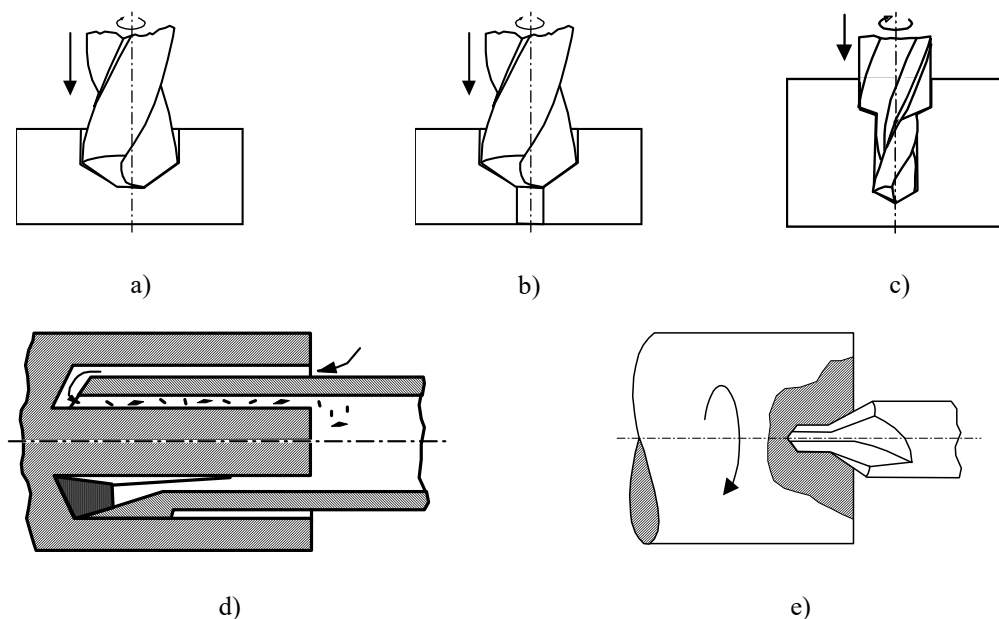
Exemplos de furação (Adaptado de [3]) – a) Furação a cheio, b) Furação com escalonada, c) Furação com rebaixo, d) Trepanação, e) Furo de ponto.
